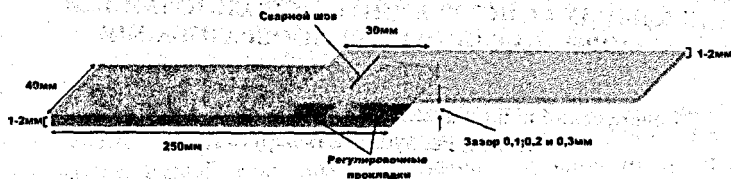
Схема процесса сварки «внахлест»
